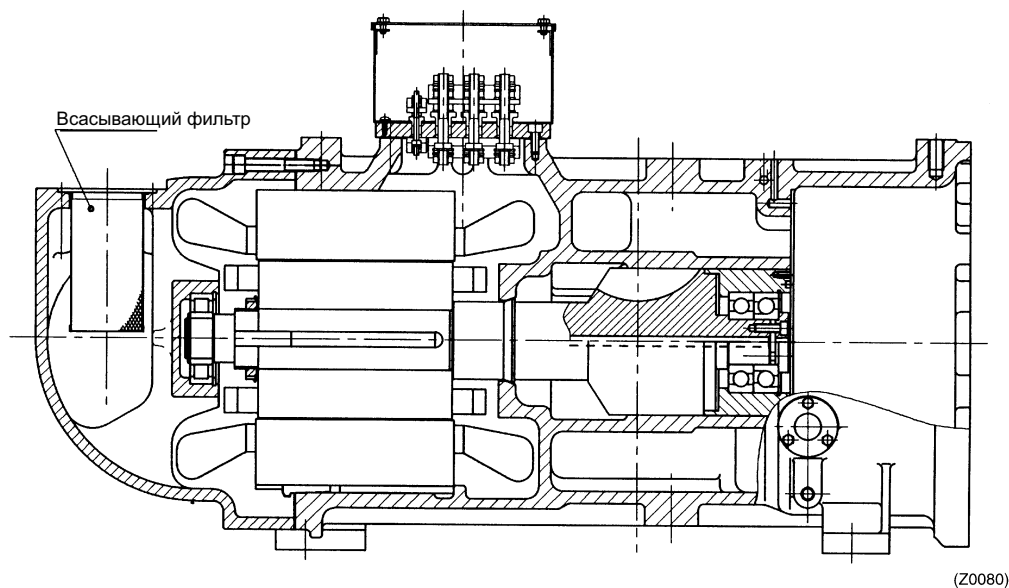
Место расположения всасывающего фильтра (поперечный разрез корпуса)
